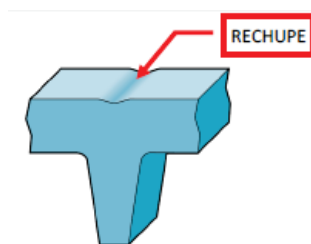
Exemplo de rechupe causado por nervura mal dimensionada (Part and Mold Design - A Design Guide, 2000) .
